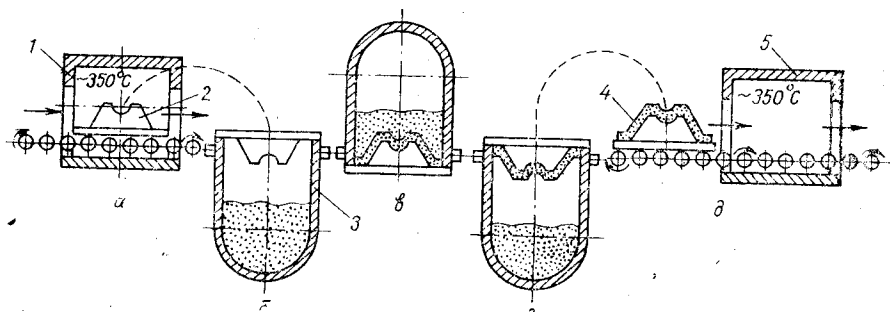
Схема виготовлення оболонкової форми (а-д):
